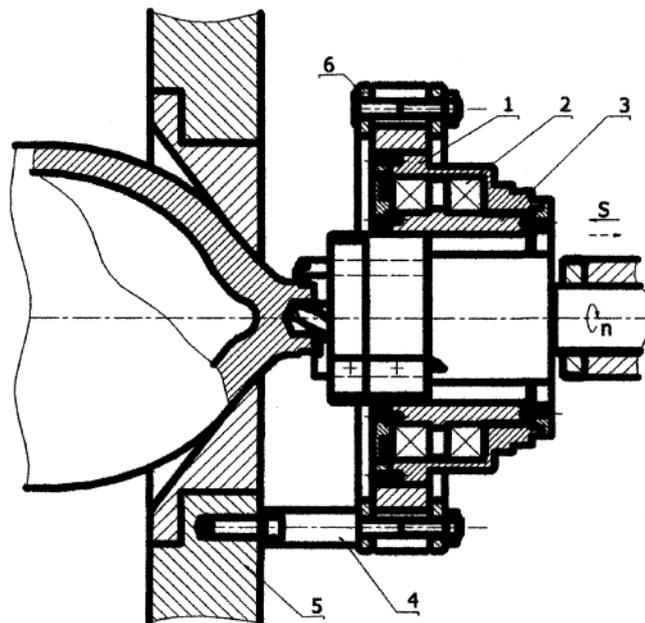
Кондуктор: 1 – корпус; 2 – подшипник качения; 3 – кондукторная втулка; 4 – анкерный болт; 5 – базирующий кронштейн; 6 – фланцы.
